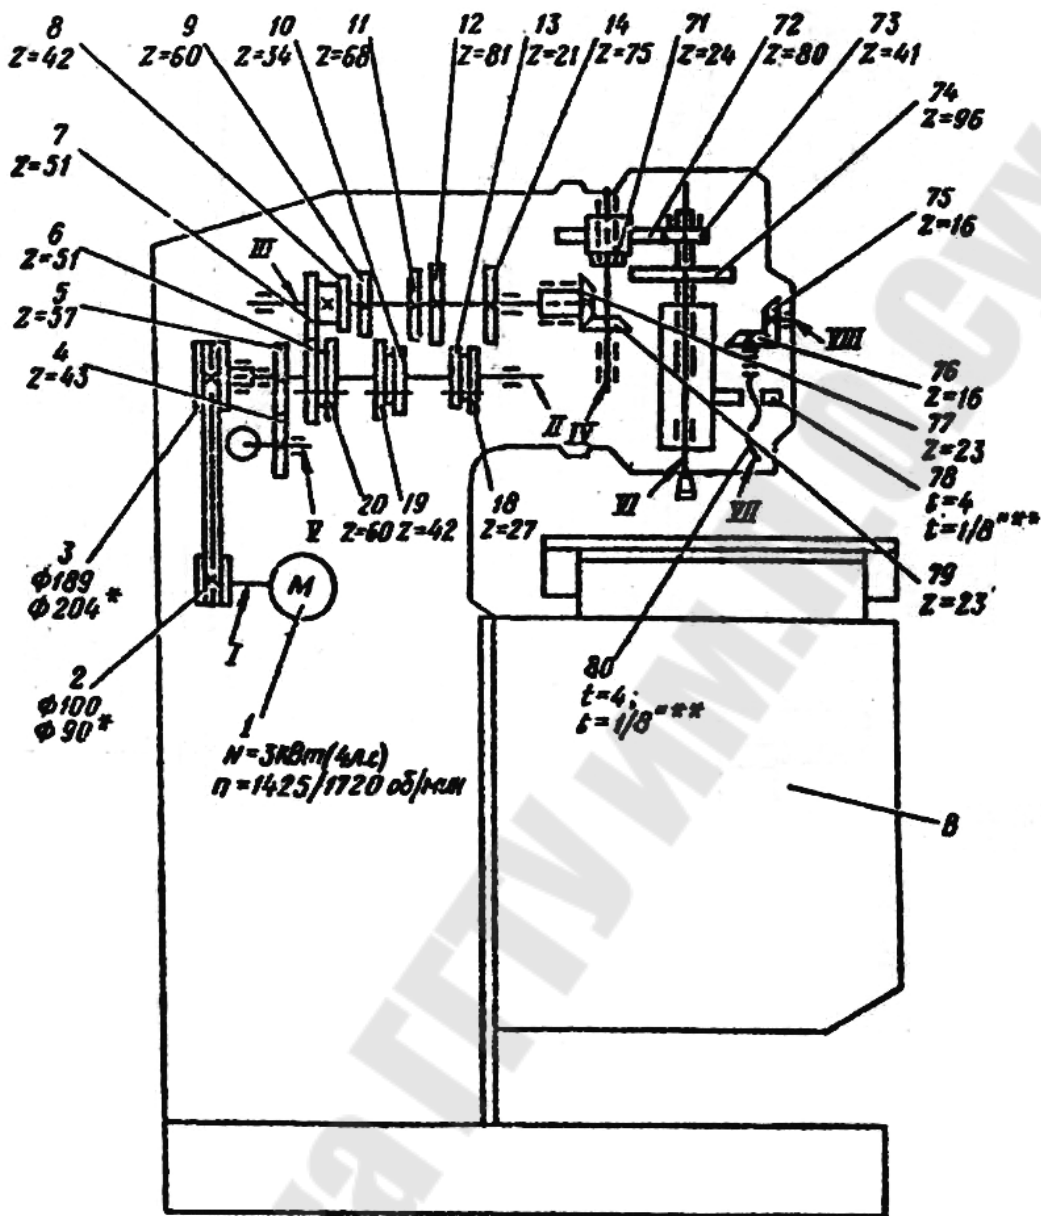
Кинематическая схема вертикально-фрезерного станка
